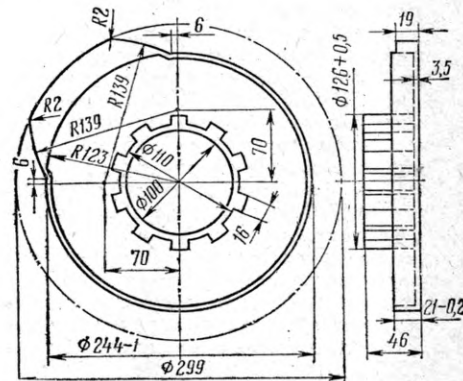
Шаблон для разметки кулачковых шайб контакторов
